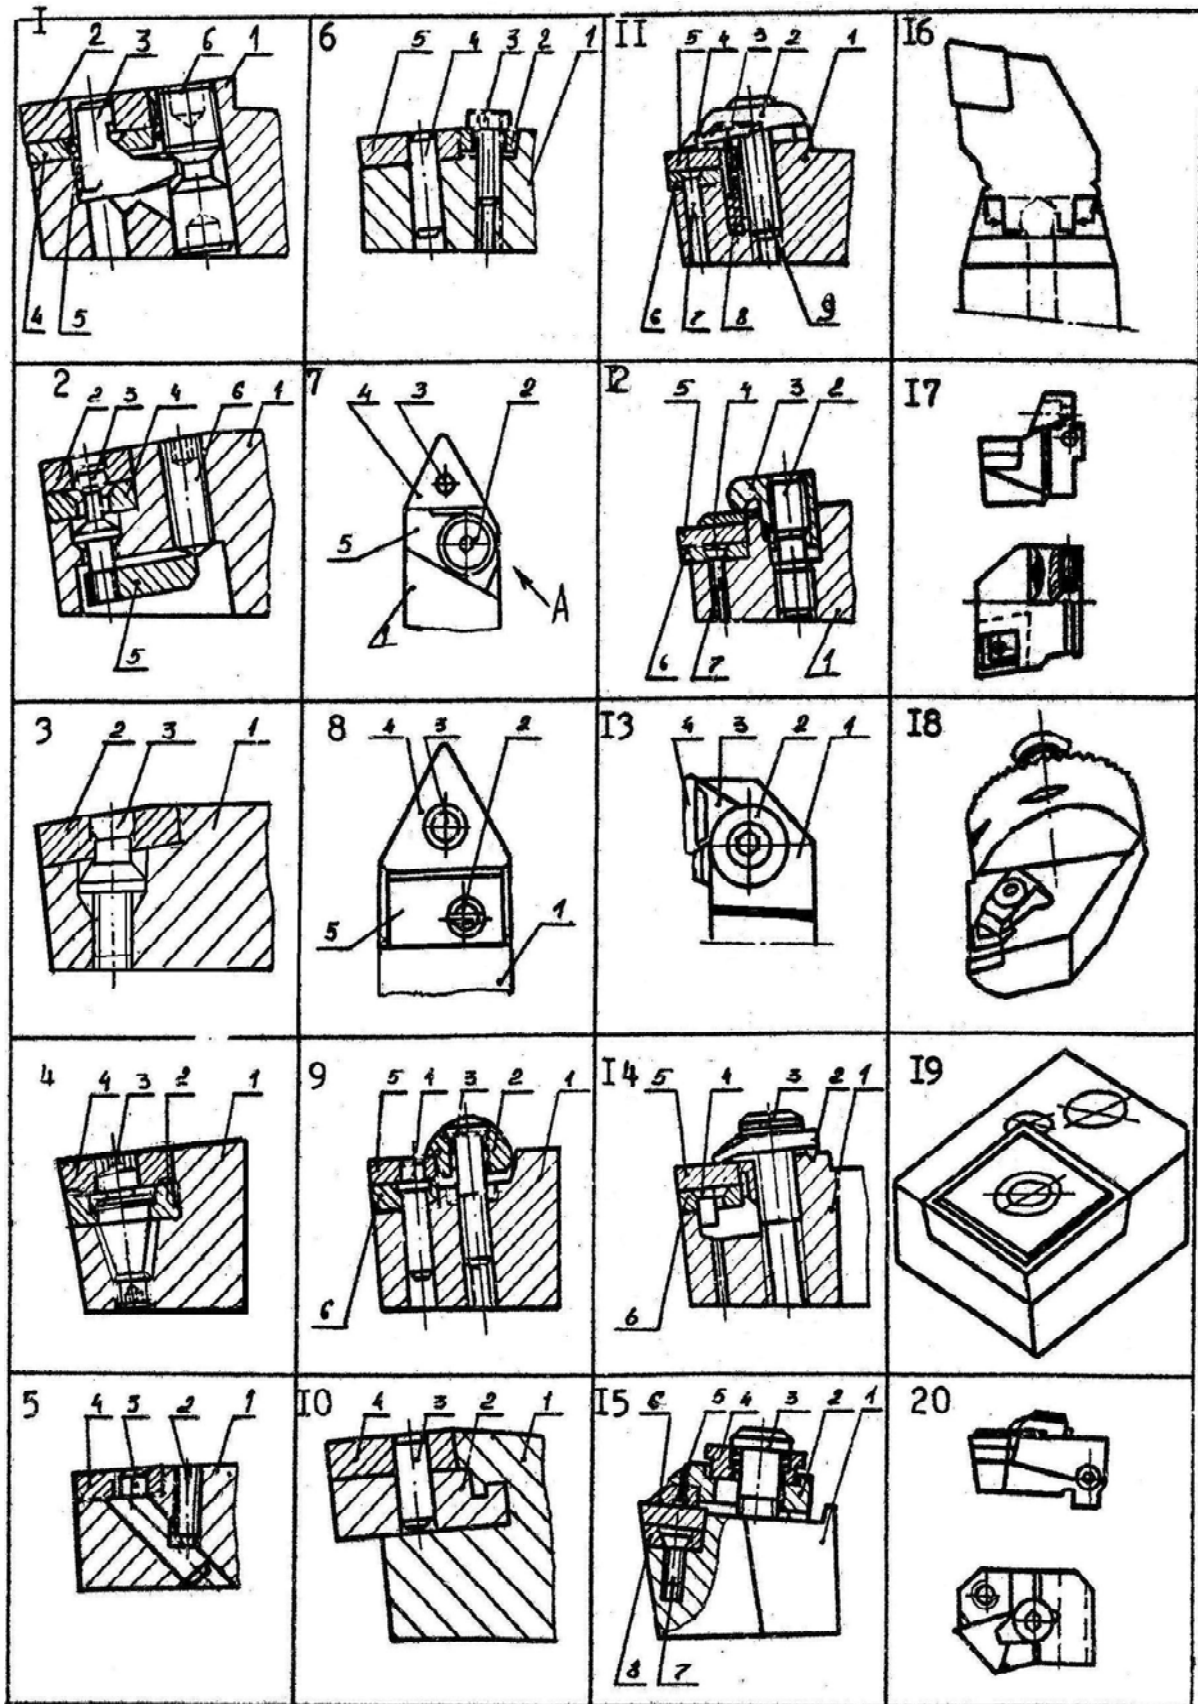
Эскизы конструкций систем крепления сборных инструментов
